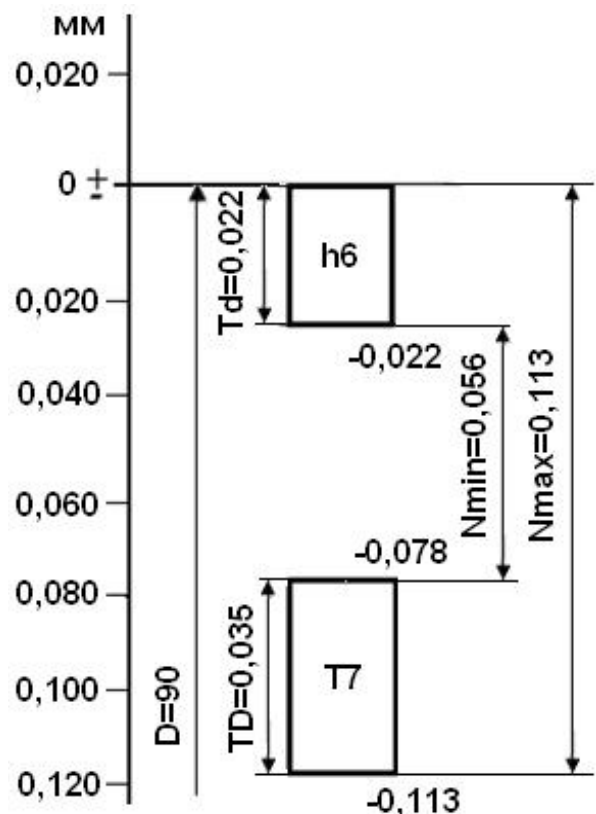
Схема розташування полів допусків деталей з'єднання $\varnothing 90\text{T7/h6}$
